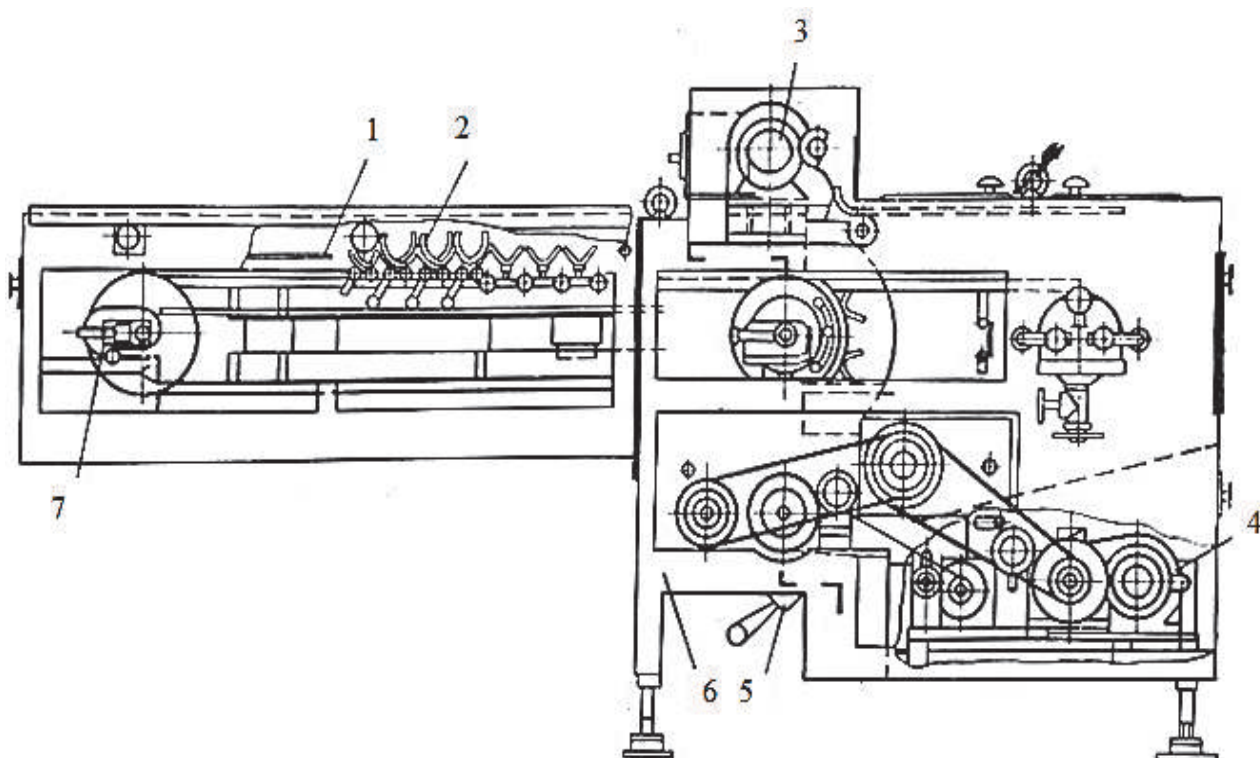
Общий вид машины ИРА-115: 1 – транспортер; 2 – захват; 3 – привод головоотрезающего ножа; 4 – привод; 5 – лоток для тушек; 6 – станина
